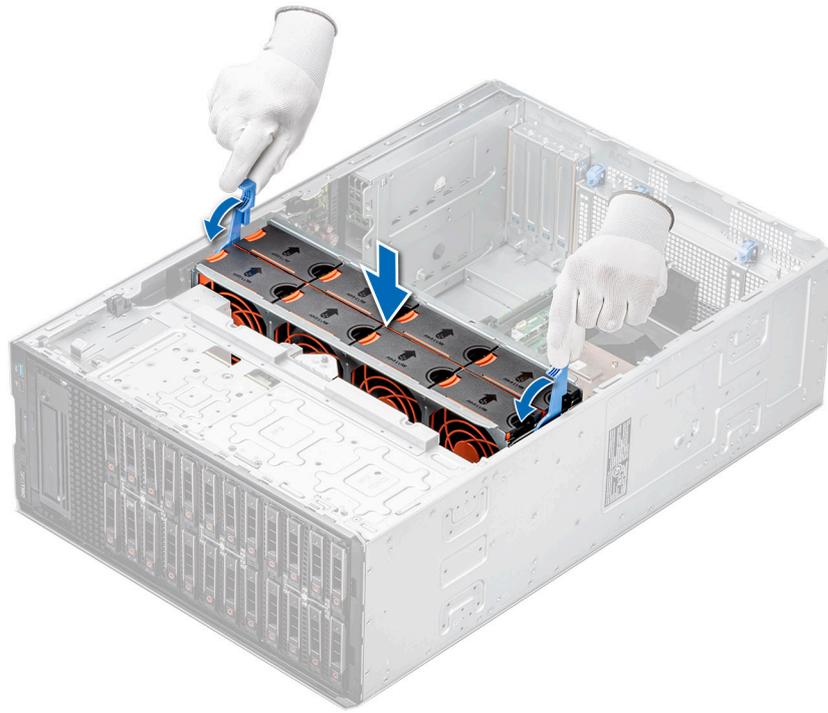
Installation d'un bâti de ventilateur de refroidissement
